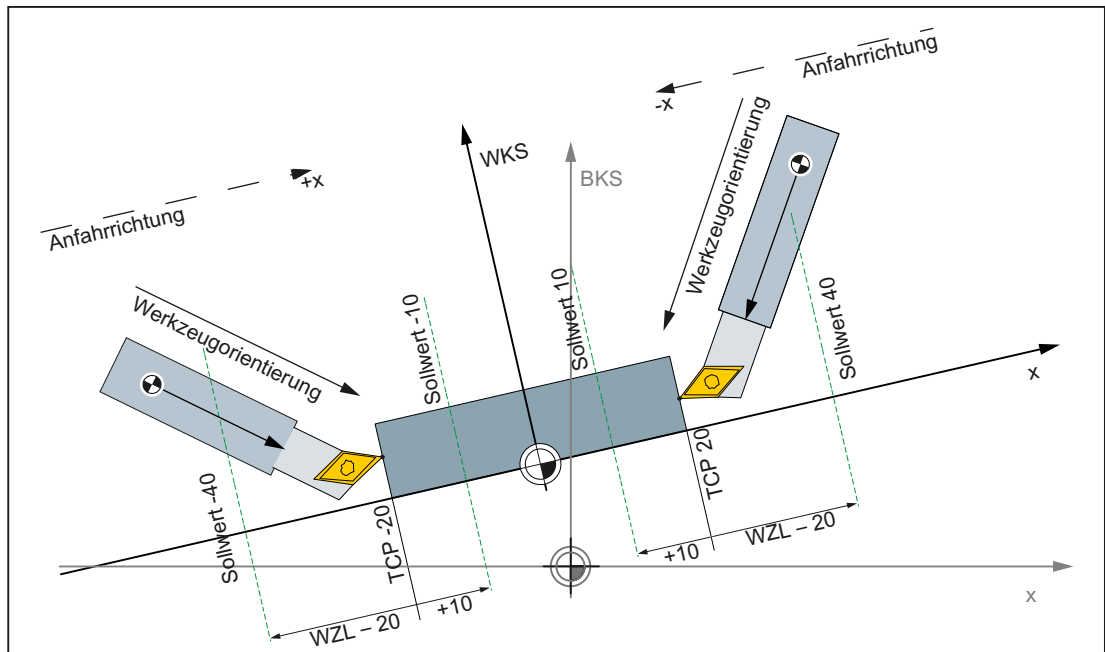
Zwei Drehwerkzeuge mit eigenem Referenzpunkt
